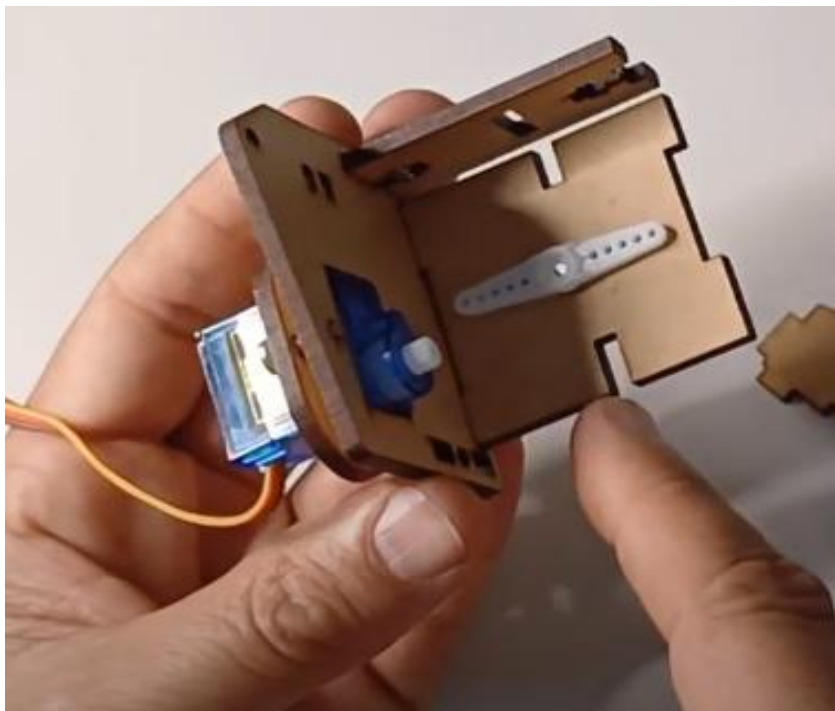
Montagem do Motor III, Suporte II, Montagem da Estrutura II e Montagem da Estrutura III- União das peças
